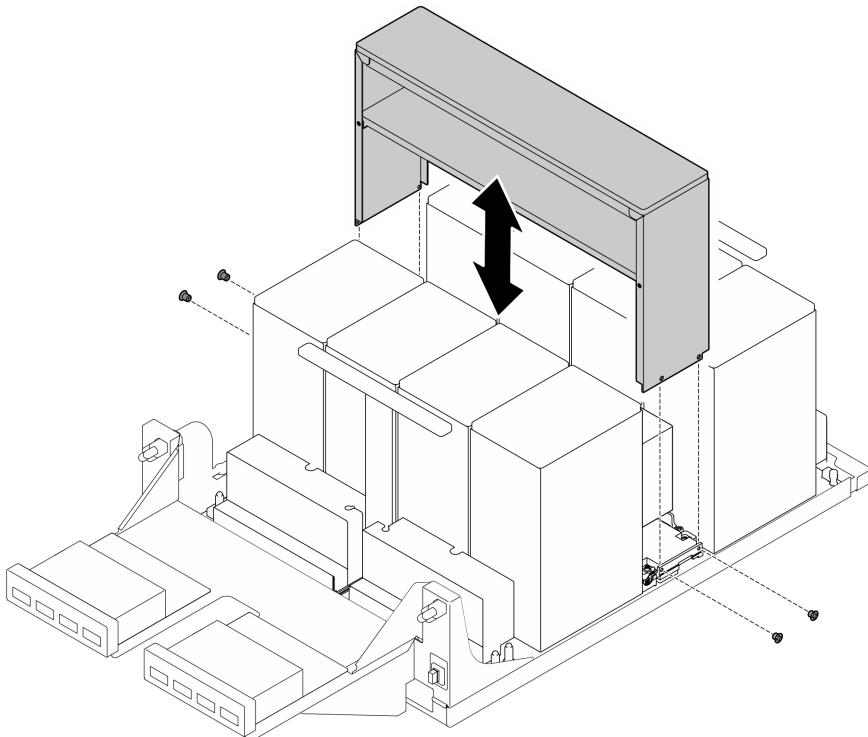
Installation du cache du dissipateur thermique NVSwitch
